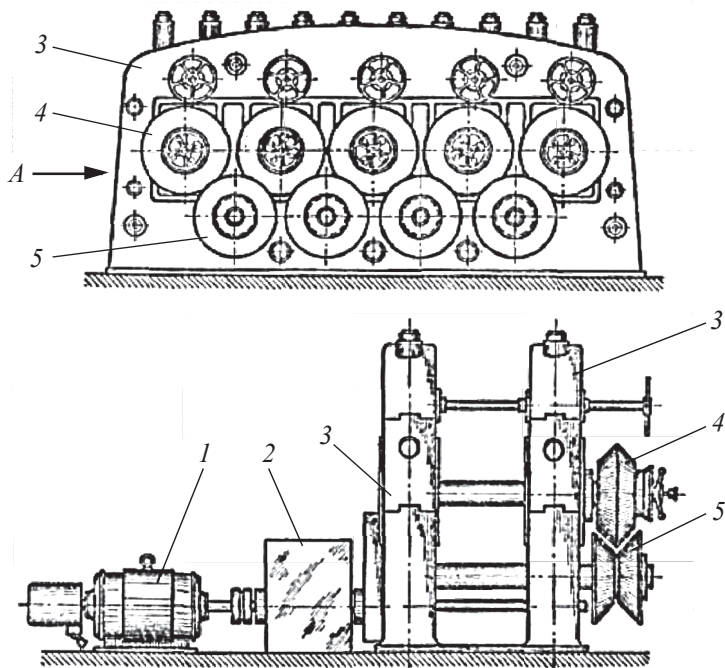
Провка детали с помощью углоправильной машины Wagner, для которой наибольший размер обрабатываемого уголка 150×20 мм:
